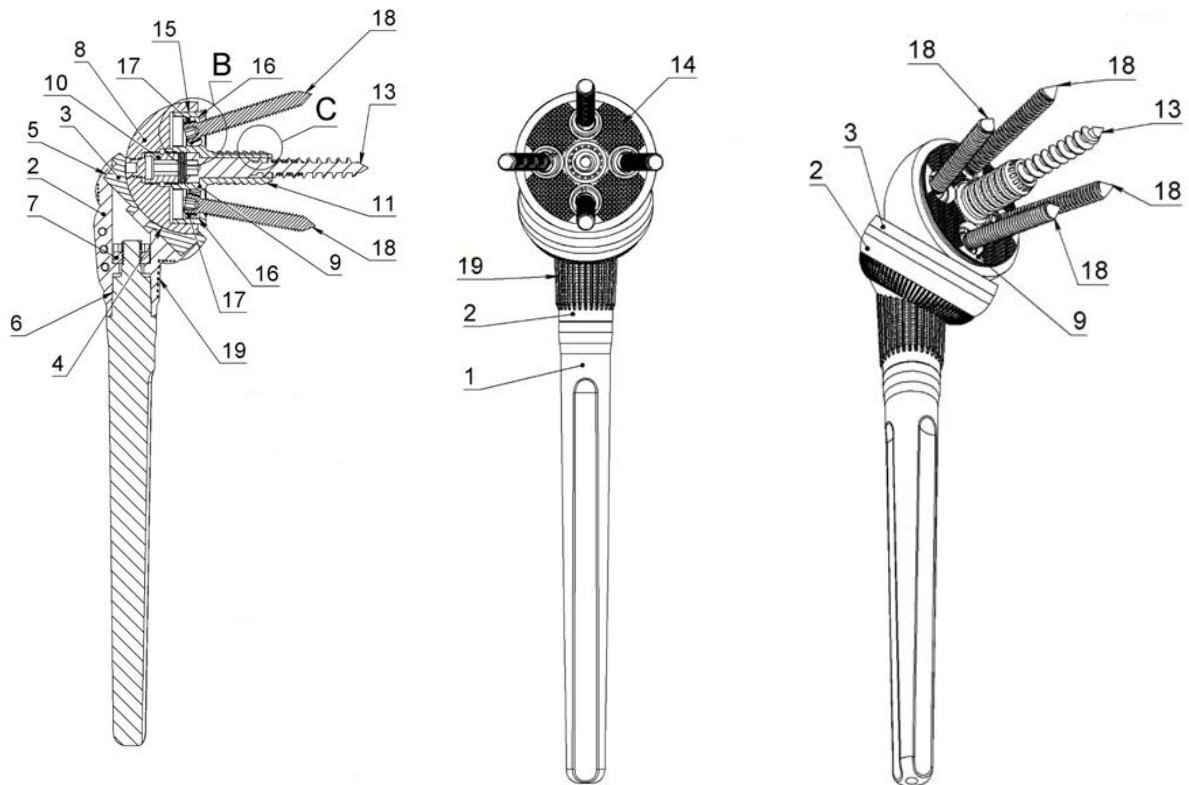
Реверсивний модульний ендопротез плечового суглоба: 1 – ніжка, що виготовлена у вигляді конусного трьохлопаткового стрижня; 2 – пориста проксимальна частина, надрукована на 3Д принтері з титанового порошку (аналог ВТ-5); 3 – вкладиш, що виготовлений з РЕЕК у вигляді конічного циліндра; 4 – увігнутої сферичною поверхнею вкладиша; 5 – конус Морзе; 6 – проксимальна частина ендопротезу фіксується за допомогою конуса Морзе до проксимальної частини ніжки; 7 – фіксуюча гайка; 8 – гленоїдальна головка; 9 – гленоїдальна опорна пластина; 9 – зовнішній край опорної пластини, виконаний у вигляді конуса Морзе 10 – фіксуючий гвинт; 11 – центральний стержень; 12 – конусоподібні ребра з довжиною ребра пори 350-500 мкм; 13 – центральний гвинт; 14 – поверхня гленоїдальної опорної виконана пористою з довжиною ребра пори 350-500 мкм на глибину 2 мм; 15 – зовнішня поверхня гленоїдальної опорної пластини виконана у вигляді конуса Морзе; 16 – сферичні отвори гленоїдальної опори; 17 – сферичні шайби; 18 – гвинти; 19 – проксимальна частина з ребристою пористою зовнішньою поверхнею [30].
